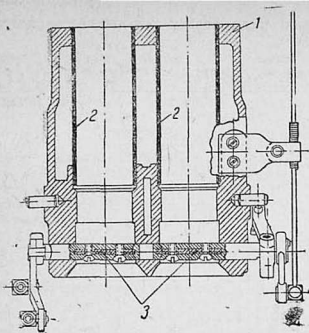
Подогреватель: 1—корпус; 2—патрубки; 3—дрессельные заслонки.
